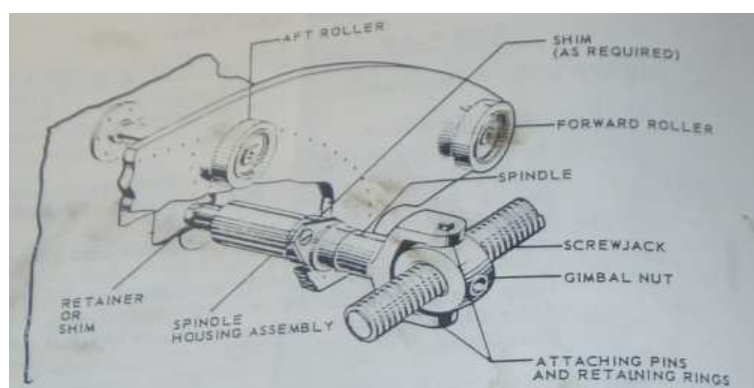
Conjunto del Spindle o Eje Giratorio corto del Flap
